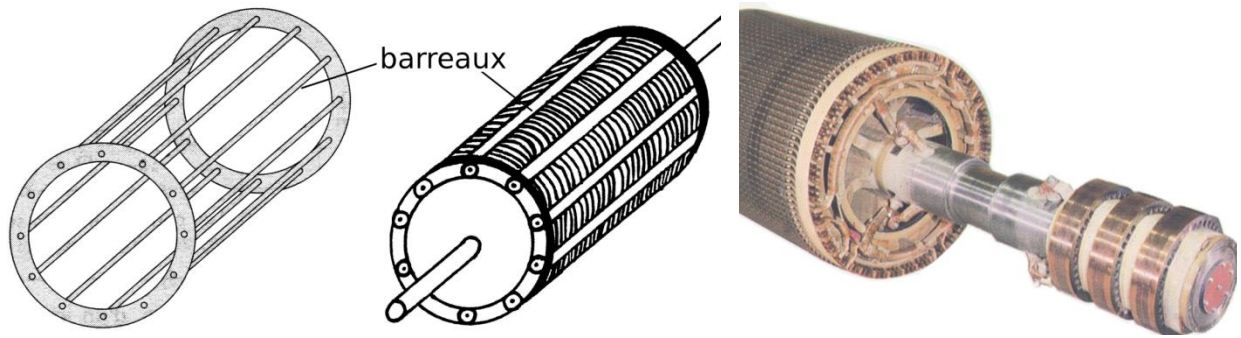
Machine asynchrone à rotor à cage et à rotor bobiné.
